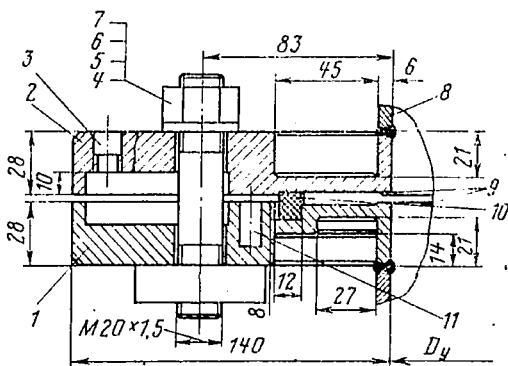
Конструкция и размеры фланцевого венца для комбинированного проволочного и резинового уплотнения крупногабаритных соединений.
